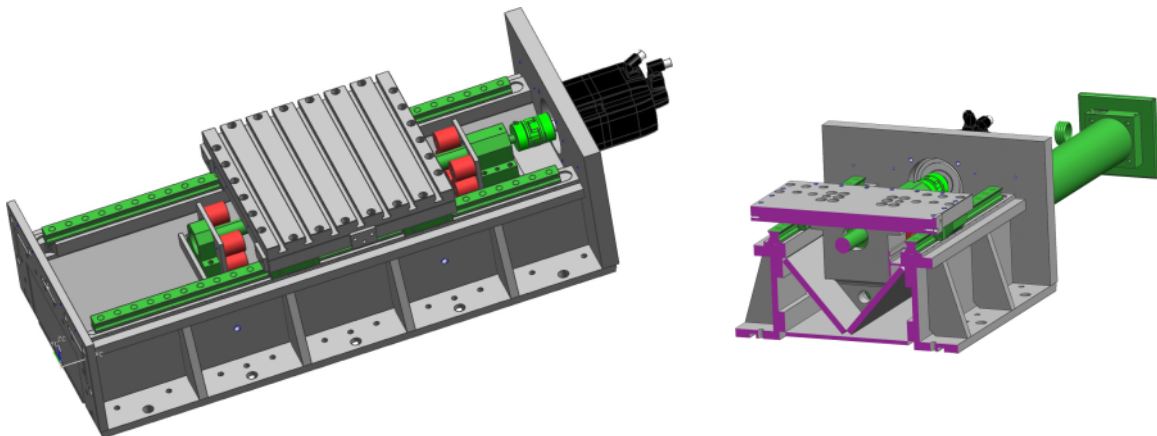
Die kurze Linearachse ist ähnlich aufgebaut wie die lange. Wegen der Kolbenstange für den Gewichtsausgleich kann zur Versteifung des Kastens nur ein V-Profil eingeschweisst werden.
